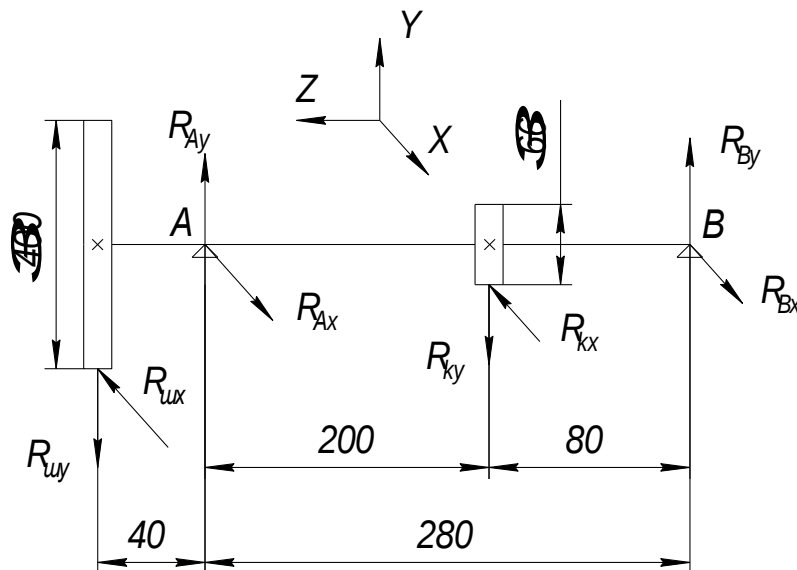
Розрахункова схема першого вала коробки швидкостей
